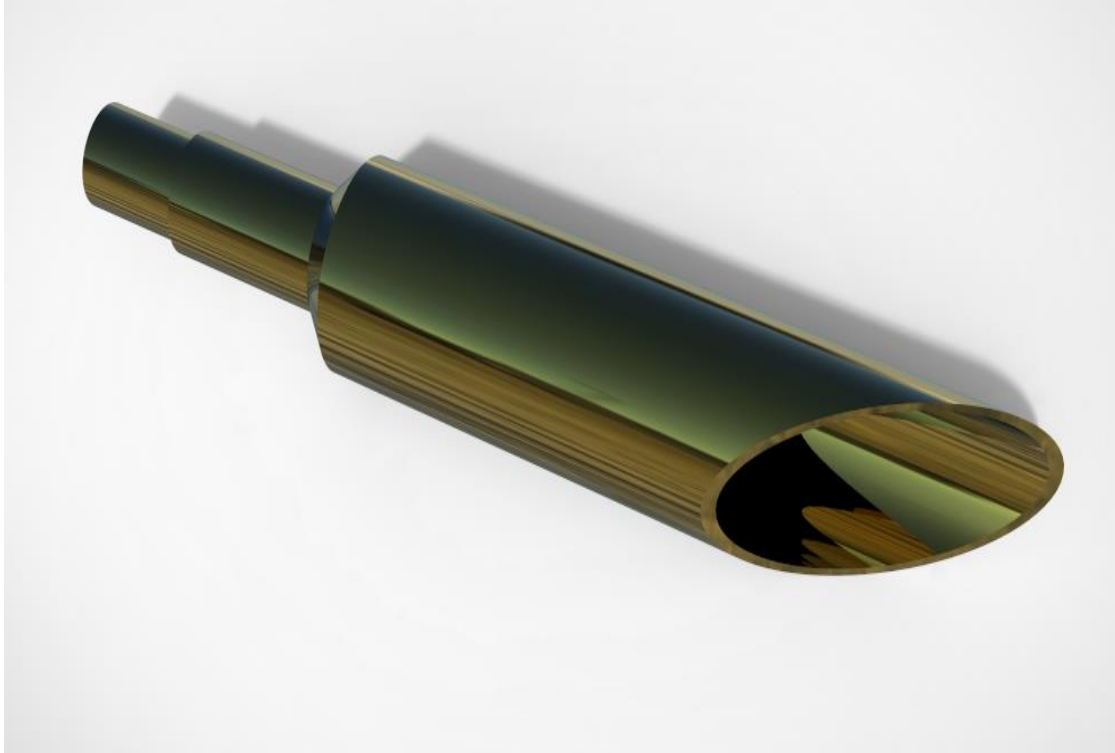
Exhaust Pipe. Tras renderizado
